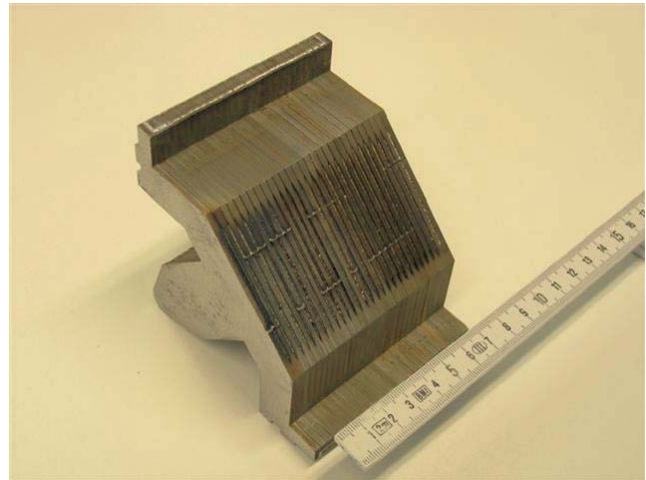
TQG-Quadrupolquadrant aus VACOFER. Bearbeitung mit Wasserstrahlschneidetechnik und Elektronenstrahlschweißung der Lamellen.
